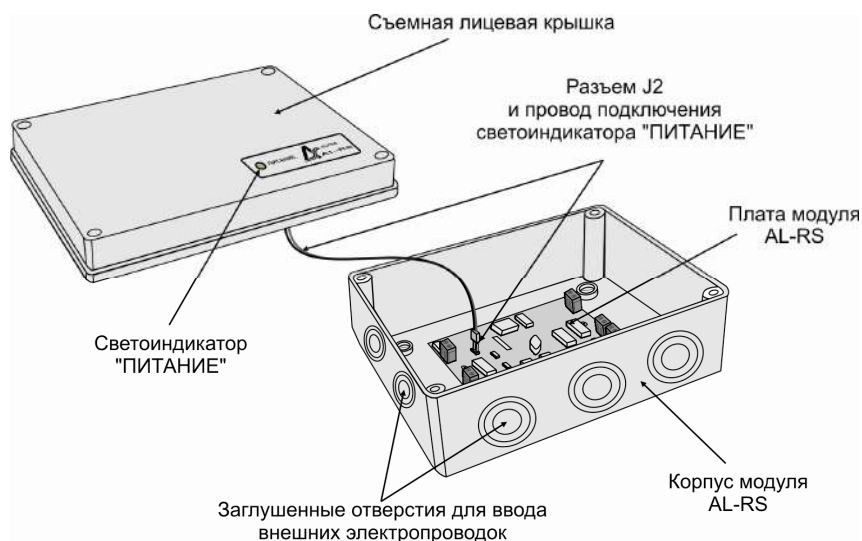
Общий вид модуля AL-RS (лицевая крышка корпуса снята)
